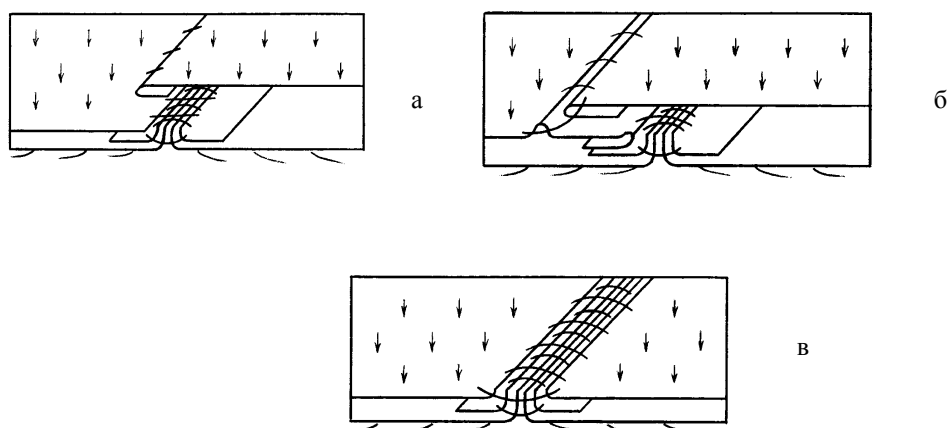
Монтажные схемы вариантов прикрепления утепляющей прокладки по пройме изделия
